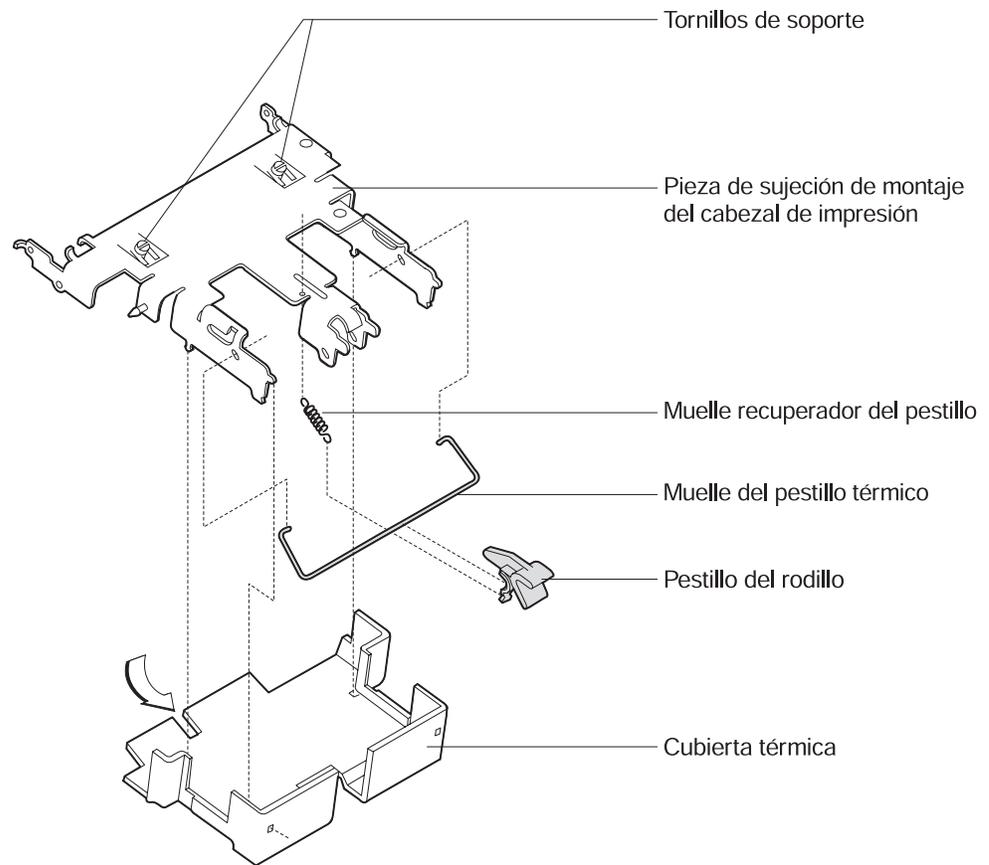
Conjunto del pestillo del cabezal de impresión térmica
